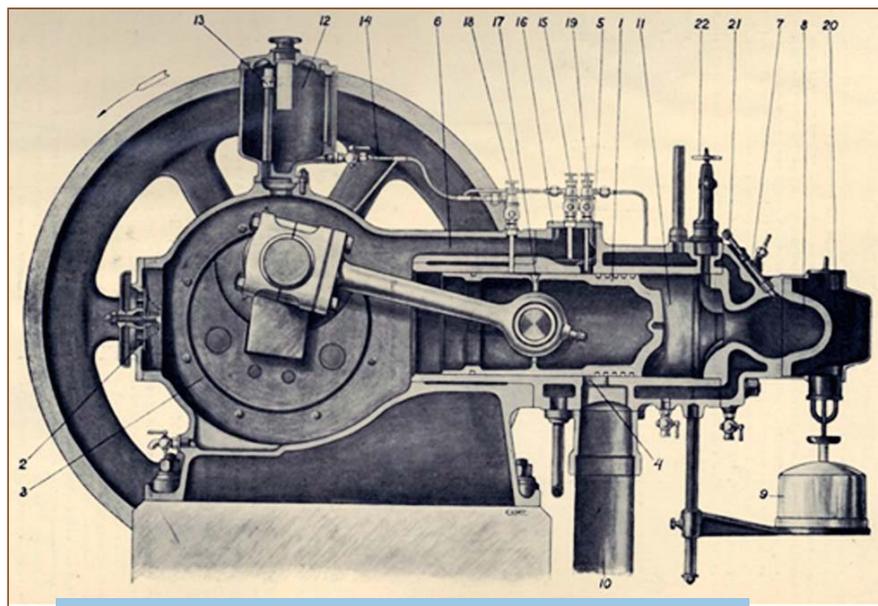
Продольный разрез нефтянки завода "Красный двигатель"
